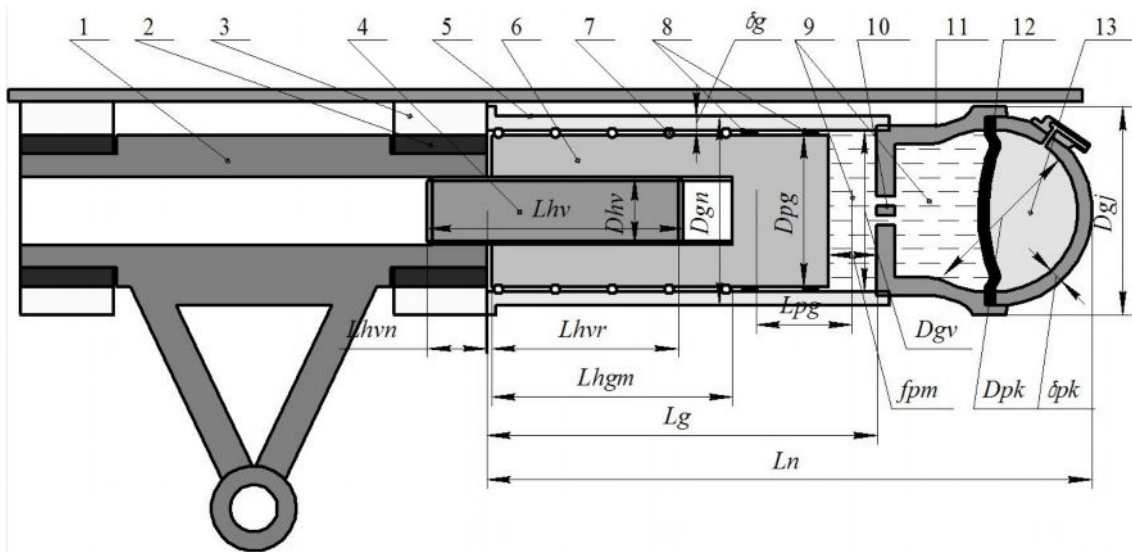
Розрахункова схема гідропневматичної ресори:
